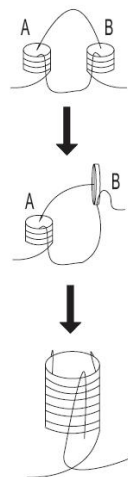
Instrucciones para cables de soldadura
